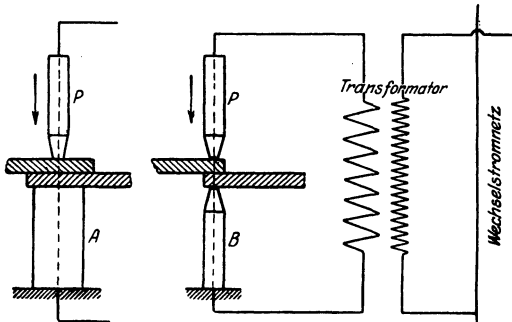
Schema der elektrischen Punktschweißung.
